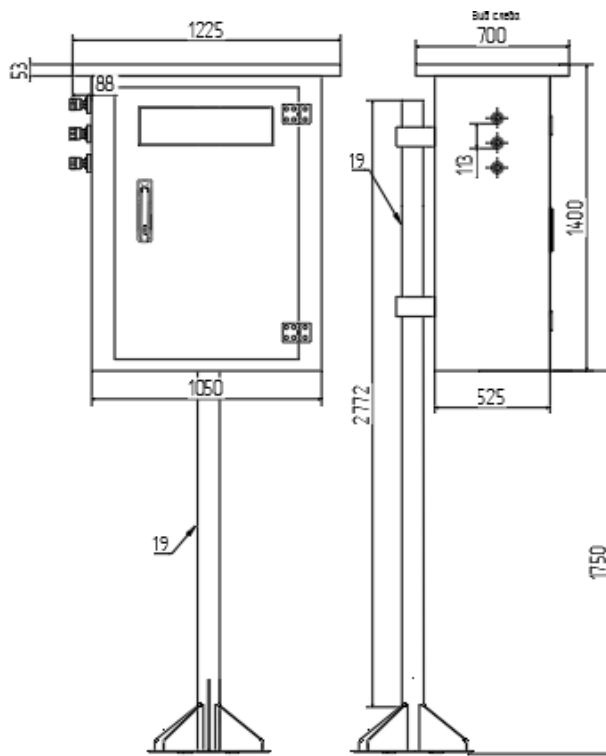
шкаф ТШВП-863. Габаритный чертеж, установленный на опоре..
